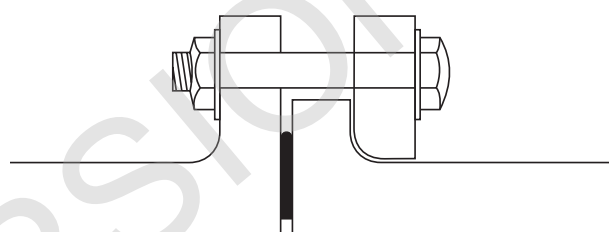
Joint à bride tournante avec joint d'étanchéité plat
